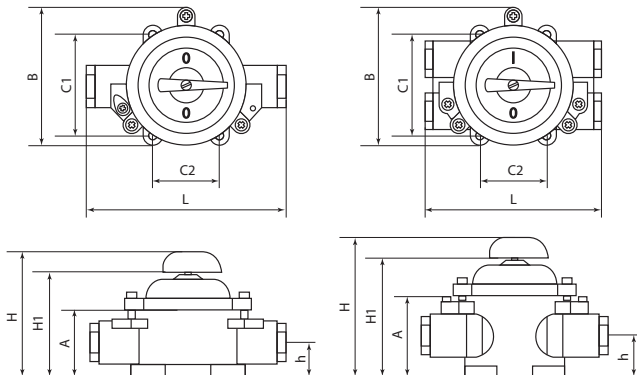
Схемы габаритных размеров пакетных выключателей и переключателей в корпусе из силумина IP56
